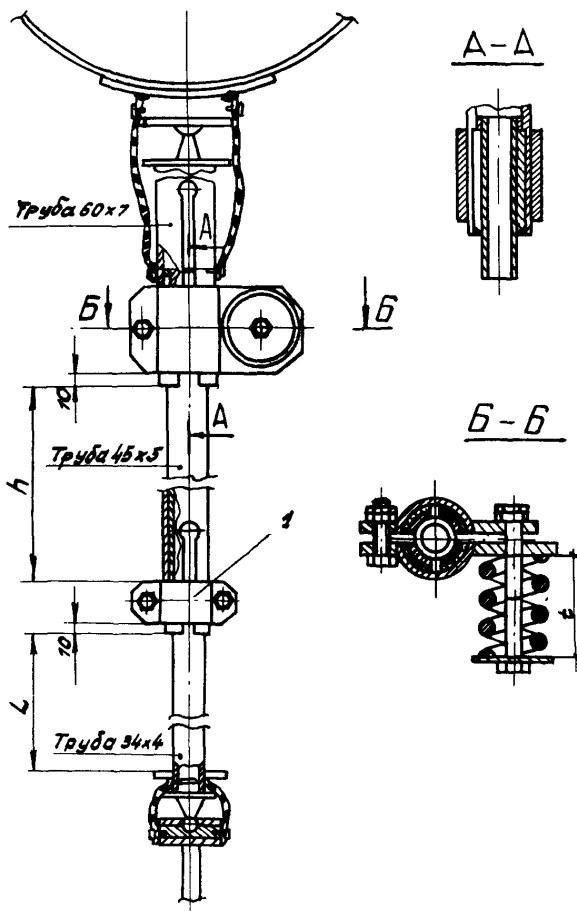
Устройство для предотвращения колебаний (одноходовое с регулируемой длиной внутренней штанги)
